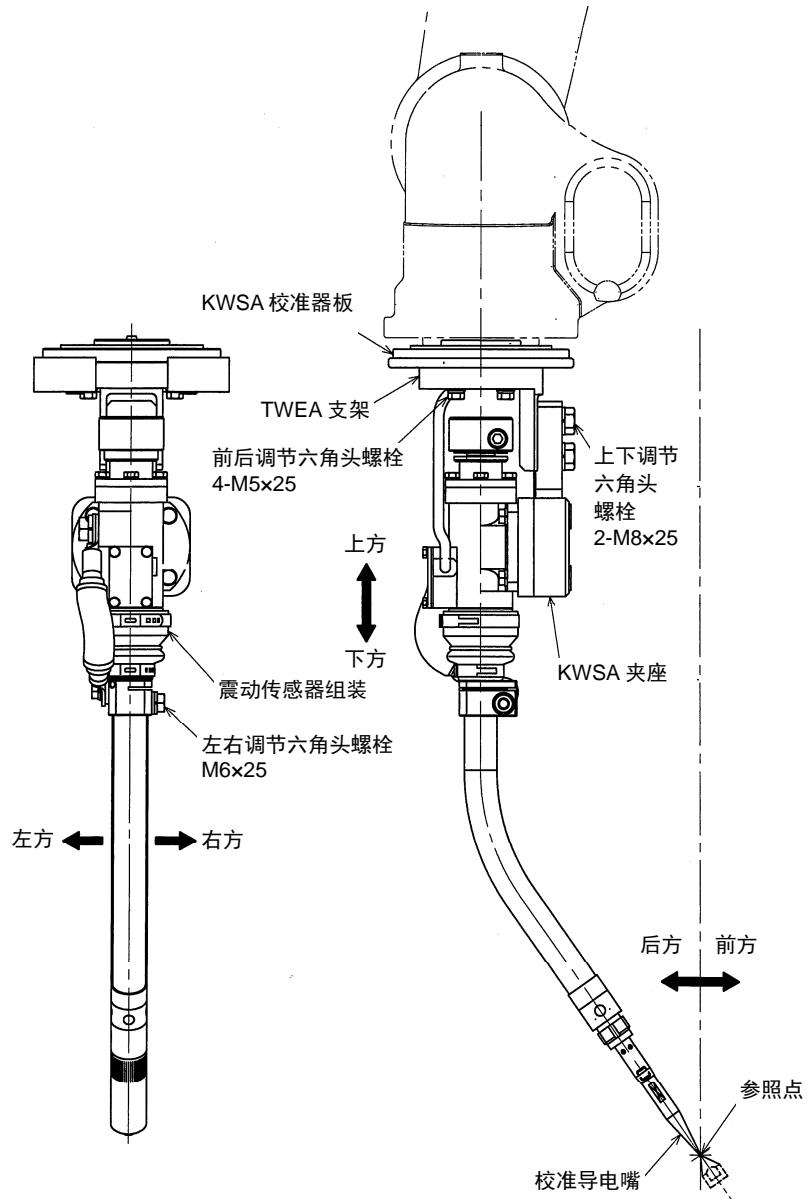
TOKIN 公司生产的焊炬的调节方法(G-type)
